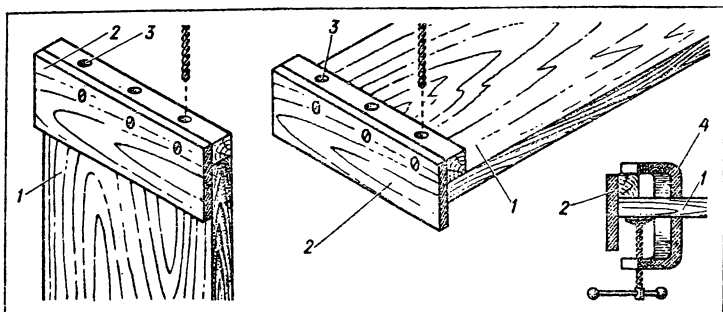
Шаблон для сверления торца и плоскости заготовки: 1 — заготовка; 2 — шаблон; 3 — отверстие в шаблоне; 4 — струбцина, которой крепится шаблон.
